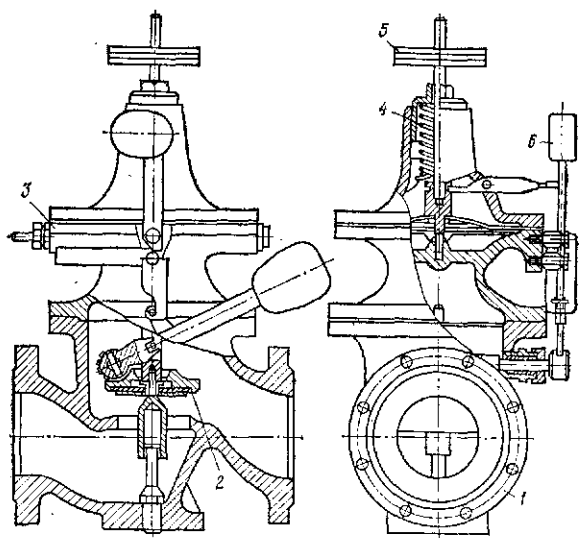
Малогабаритный предохранительный запорный клапан типа ПКН (ПКВ)
